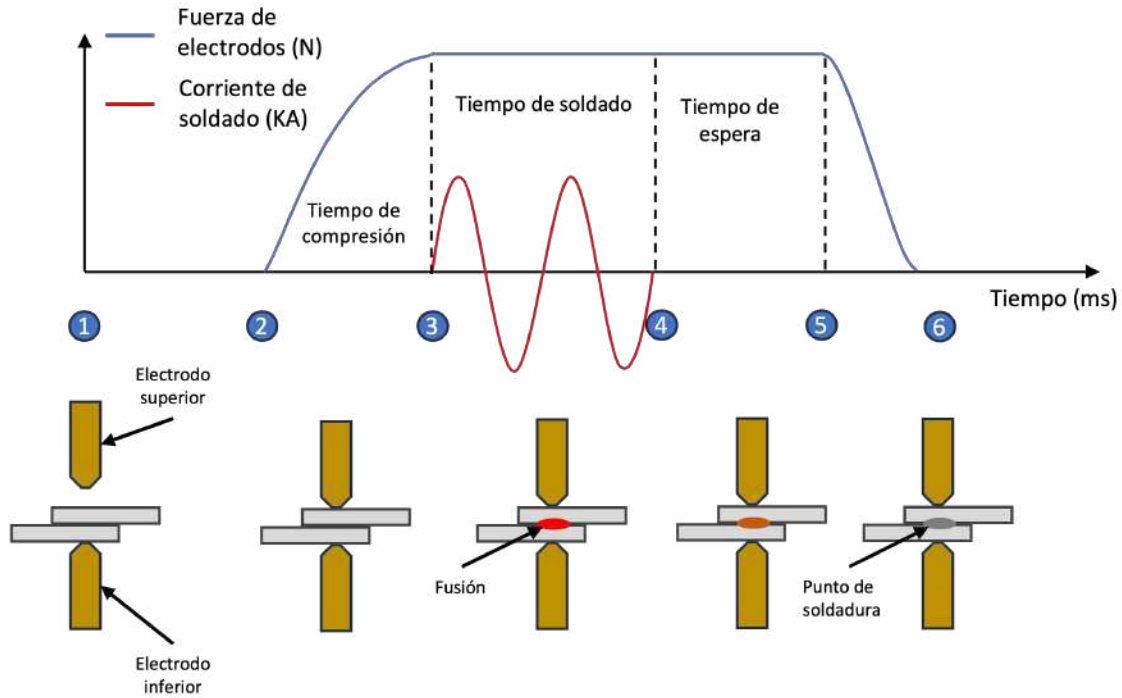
Secuencia del proceso de soldadura por puntos, adaptada de [1].
